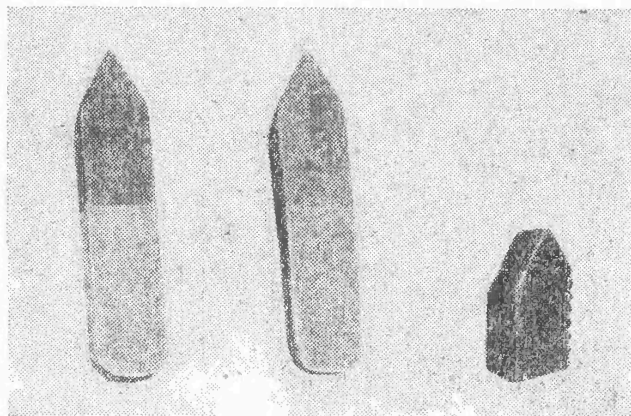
Резьбовой резец конструкции Д. И. Рыжкова.
